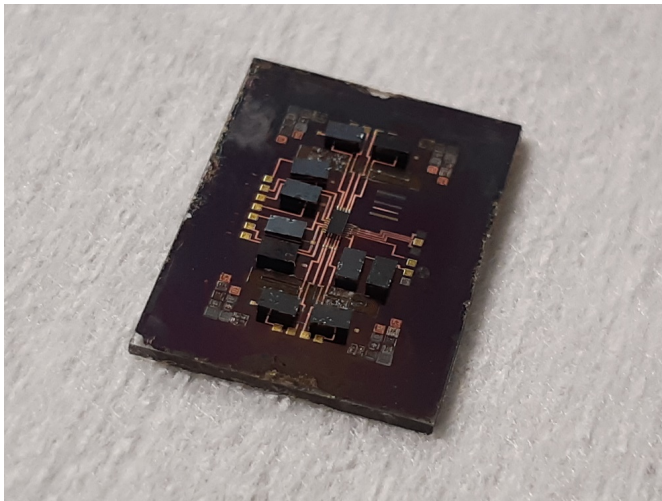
Convertisseur DC-DC intégralement fabriquée et assemblée
